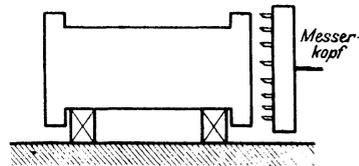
Bearbeitung der Stirnflächen der Schuhe.
